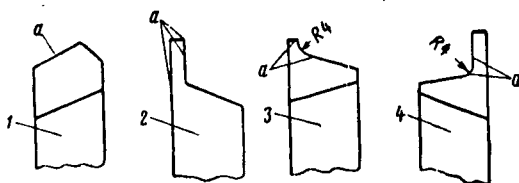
Форма режущих кромок резцов для обточки коллекторов:
